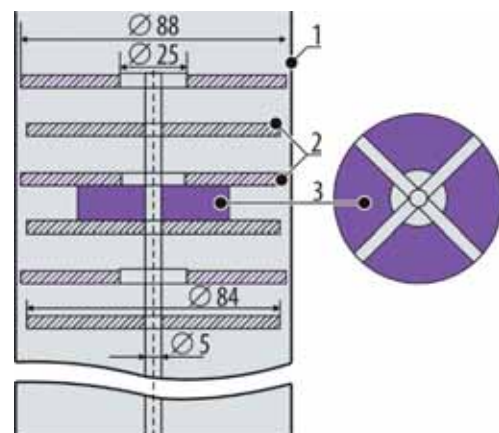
Схема макета облучательного устройства: 1 — алюминиевый корпус; 2 — диски двух типовых размеров; 3 — дистанционирующие металлические проставки
